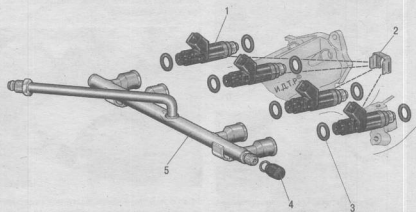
Топливная рампа и форсунки: 1 – форсунка; 2 – фиксатор форсунки; 3 – уплотнительное кольцо; 4 – штуцер для контроля давления топлива; 5 – топливная рампа
